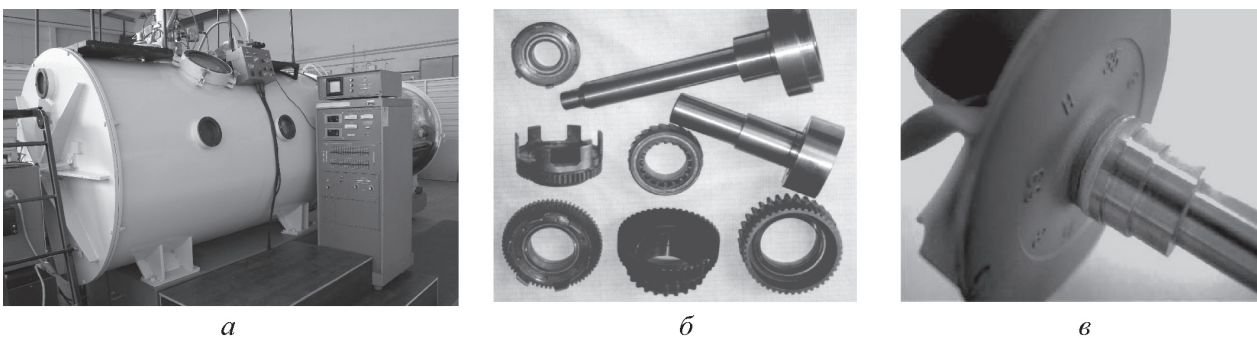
Комплекс оборудования ЭЛО (а), изготовленные с использованием ЭЛС шестерни и валы (б) и ротор турбокомпрессора (в)
